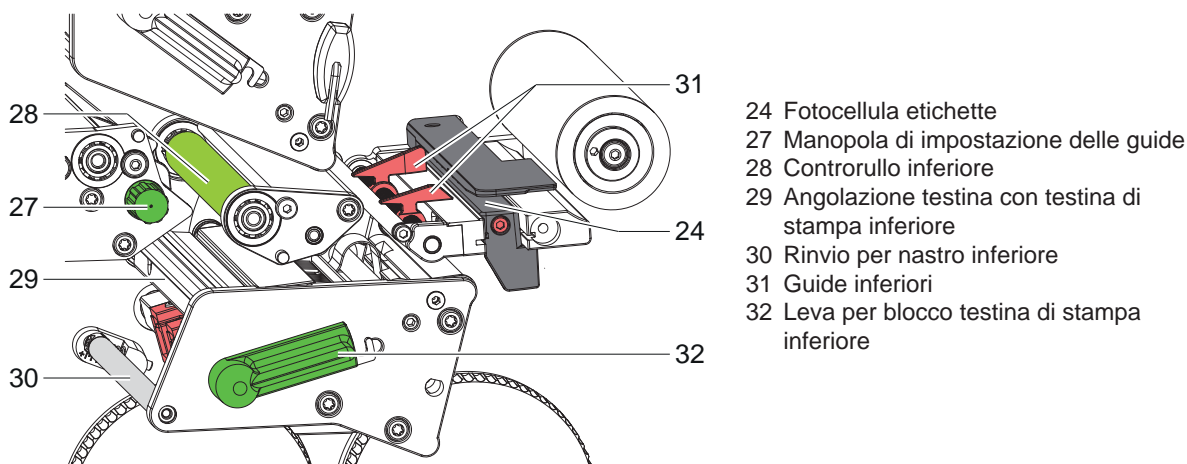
Meccanica di stampa - Gruppo di stampa inferiore
